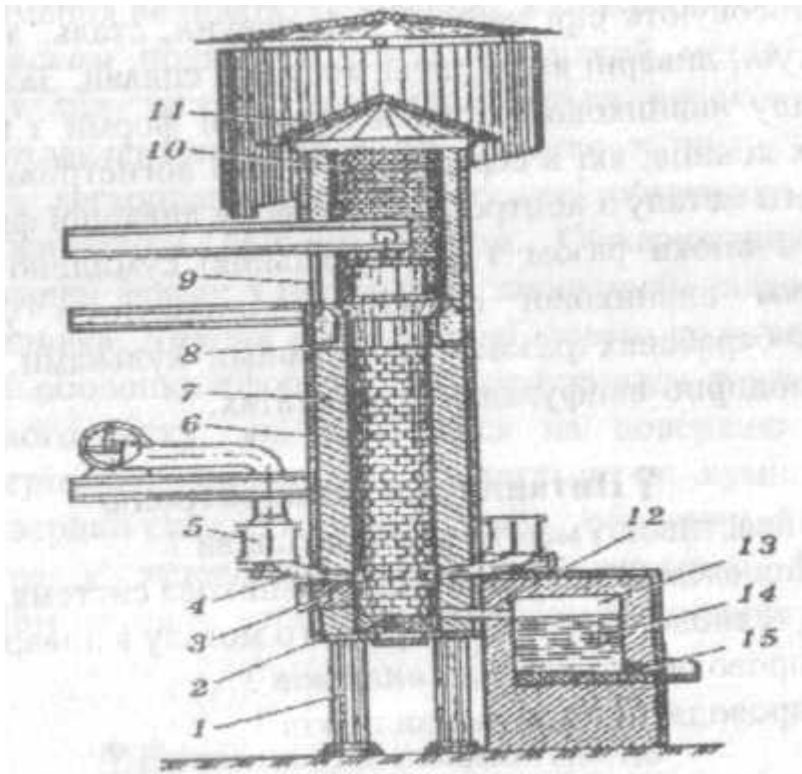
Схема вагранки: 1- чотири колони; 2 - кільцева плита; 3 - робоче вікно; 4 - фурми; 5 - кільцева коробка; 6 - сталений кожух; 7 шамотна цегла; 8 - чавунні плити; 9 - шахта з завантажувальним вікном; 10 - газовивідна груба; 11 - іскрогасник; 12 накопичувач; 13 наконичувач; 14 - шлакова льотка; 15 - чавунна льотка
